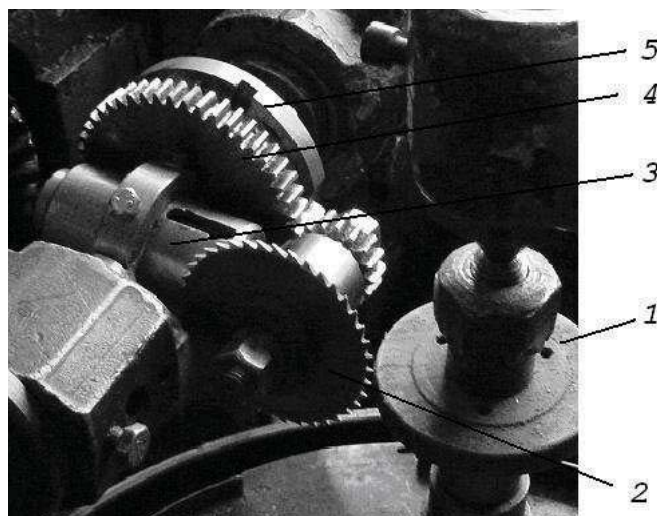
Збірна дискова фреза та спорядження зубофрезерного верстата для зубонарізання:
